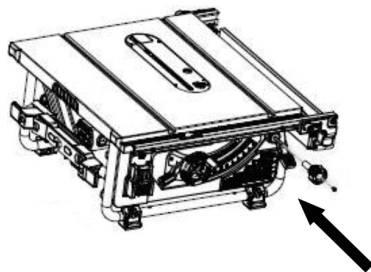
Instalando el manipulador de trabamieto del ajuste de corte
